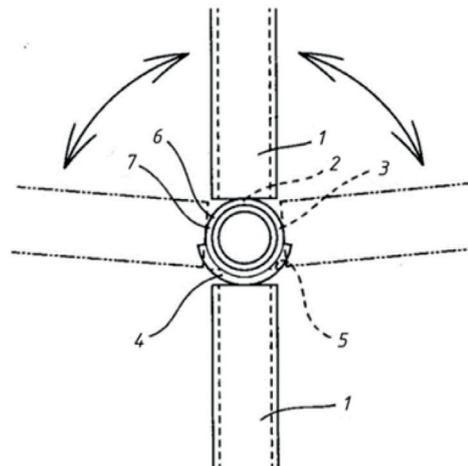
Вид узла. 1 – вертикальные стержни; 2 – муфта; 3 – центральная втулка; 4 – направляющая рама; 5 – выемка для уменьшения площади поверхности трения; 6 – концевая соединительная муфта; 7 – концевая соединительная муфта
